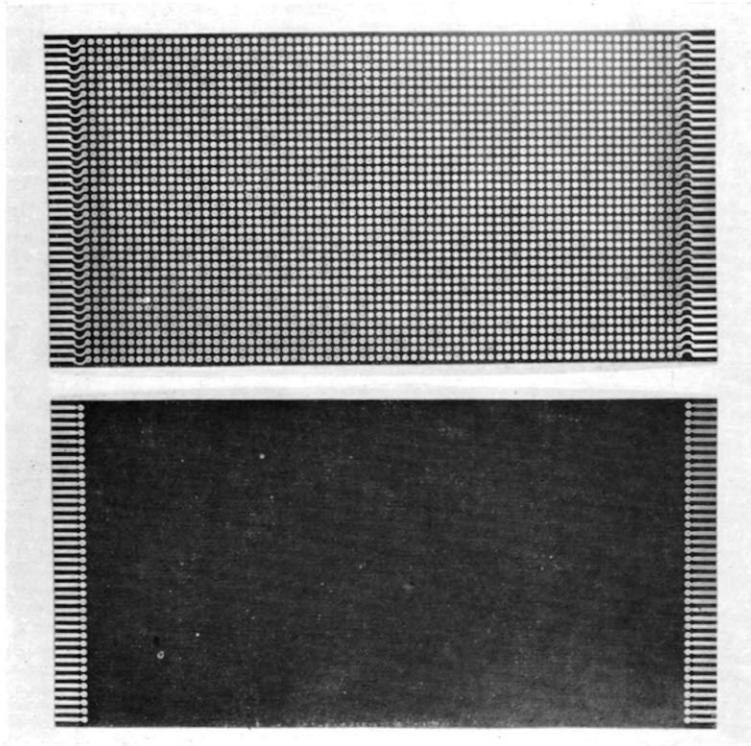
Vue recto verso de la plaque d'expériences à câblage imprimé.
